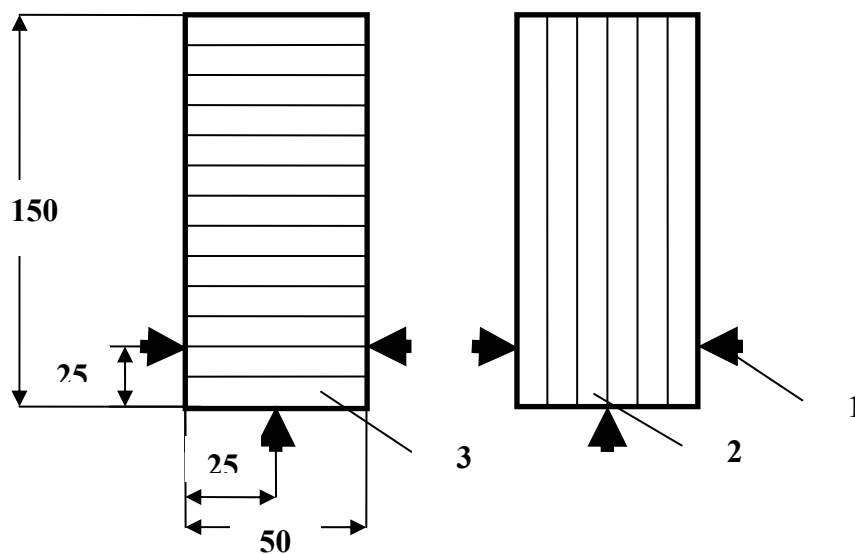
Схема измерения образцов: 1 – образец в поперечном направлении; 2 – образец в продольном направлении; 3 – точка измерения
